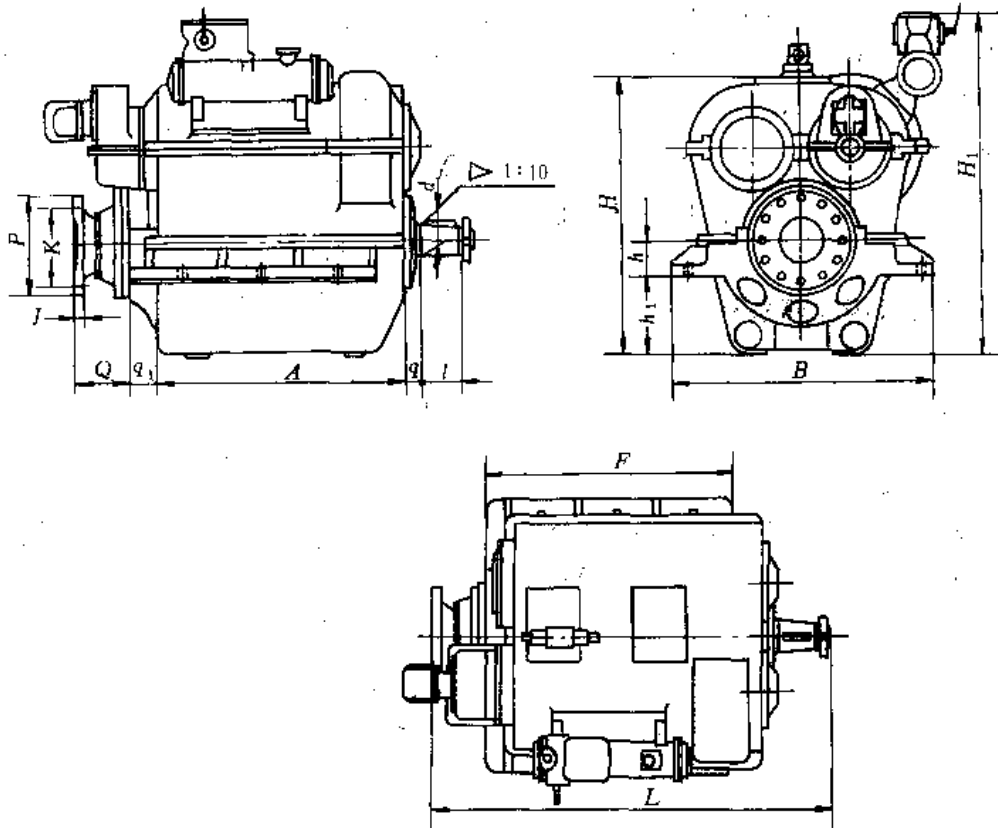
GWC、GWL 系列齿轮箱外形结构和尺寸图
